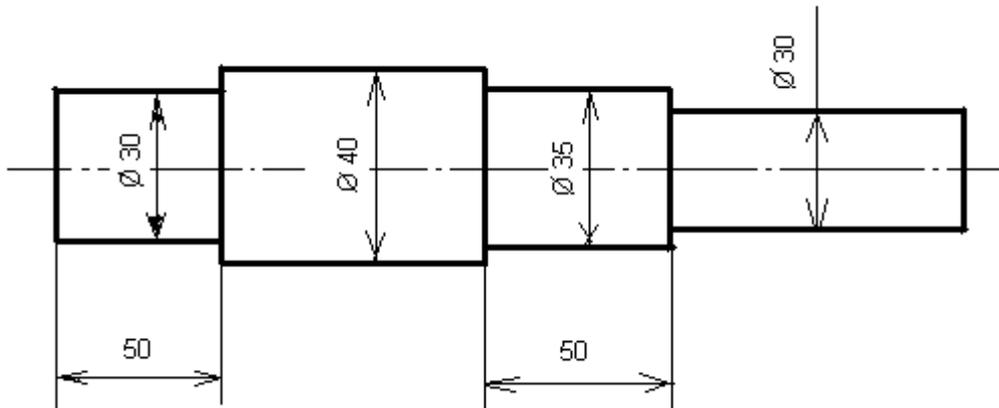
Эскиз детали «Вал», материал – сталь 40Х.
